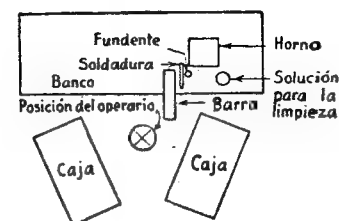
Disposición del lugar de trabajo para soldar cajas metálicas rectangulares.
